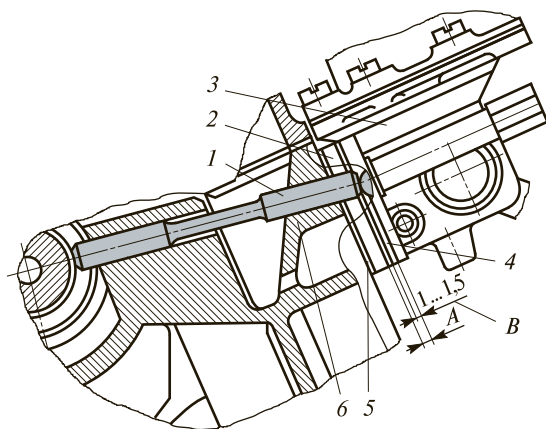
Схема для контроля и регулировки выступания толкателя привода насоса двигателя УЗАМ:
